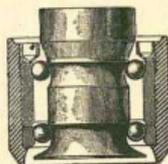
Шаровой подшипникъ у сепаратора Корона С.
